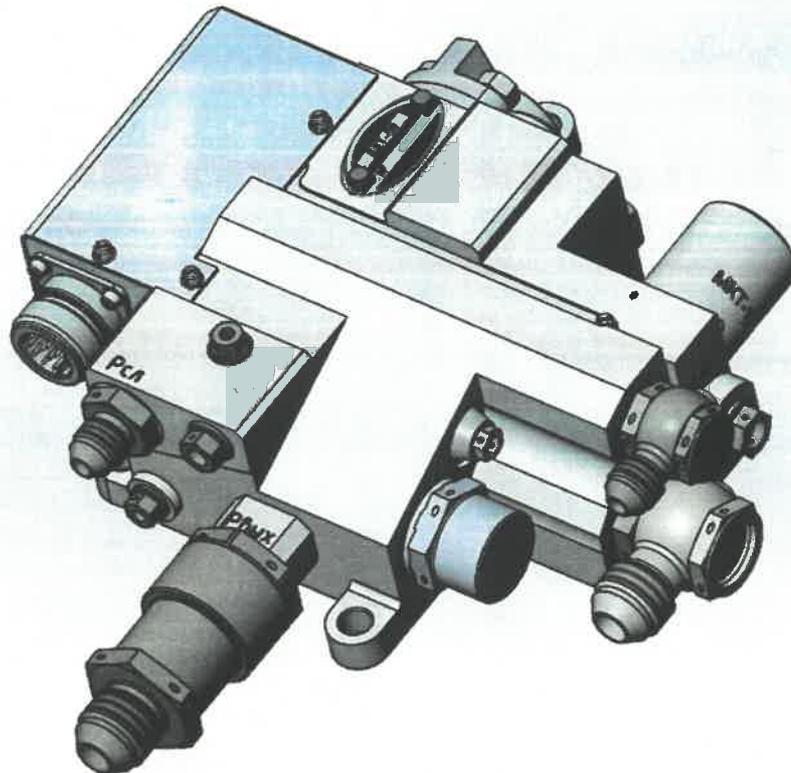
Общий вид дополнительного дозатора топлива ДДТ-59
